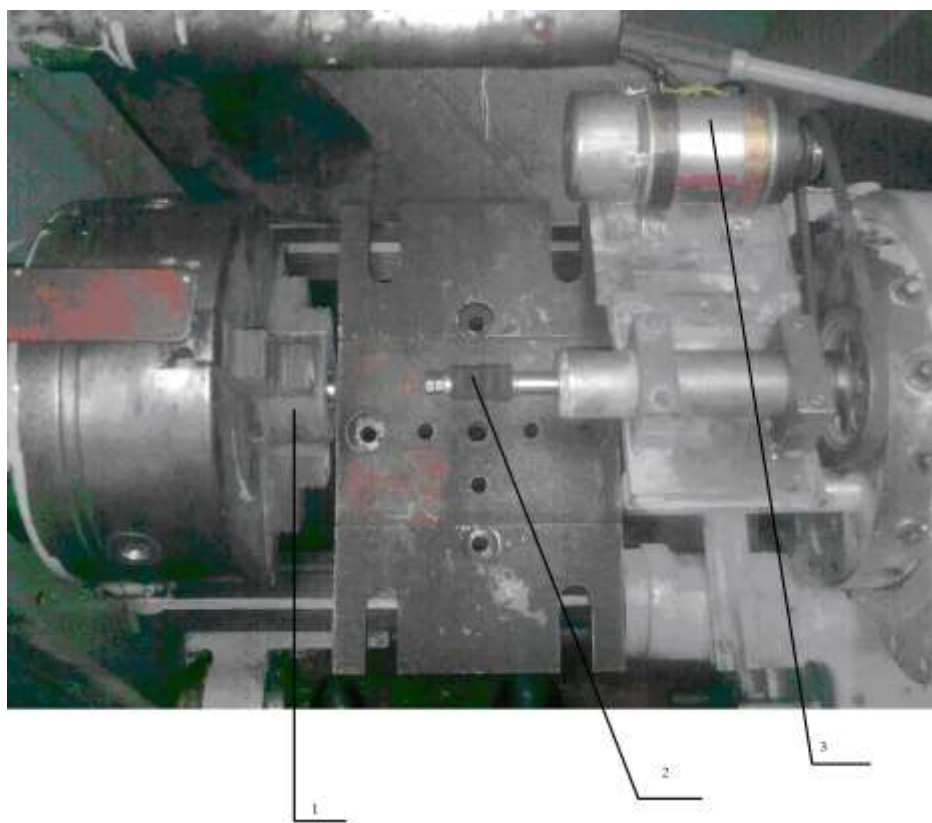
Общий вид приспособления для магнитно-абразивной обработки
